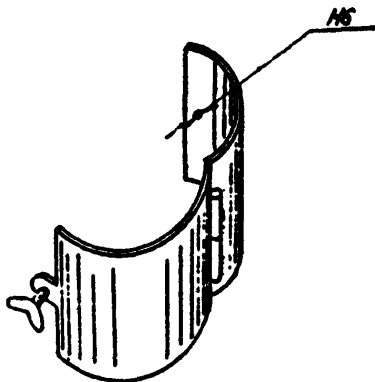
Кожух для защиты изоляторов при сварке секций токопровода ТЭК-10 в блоки
